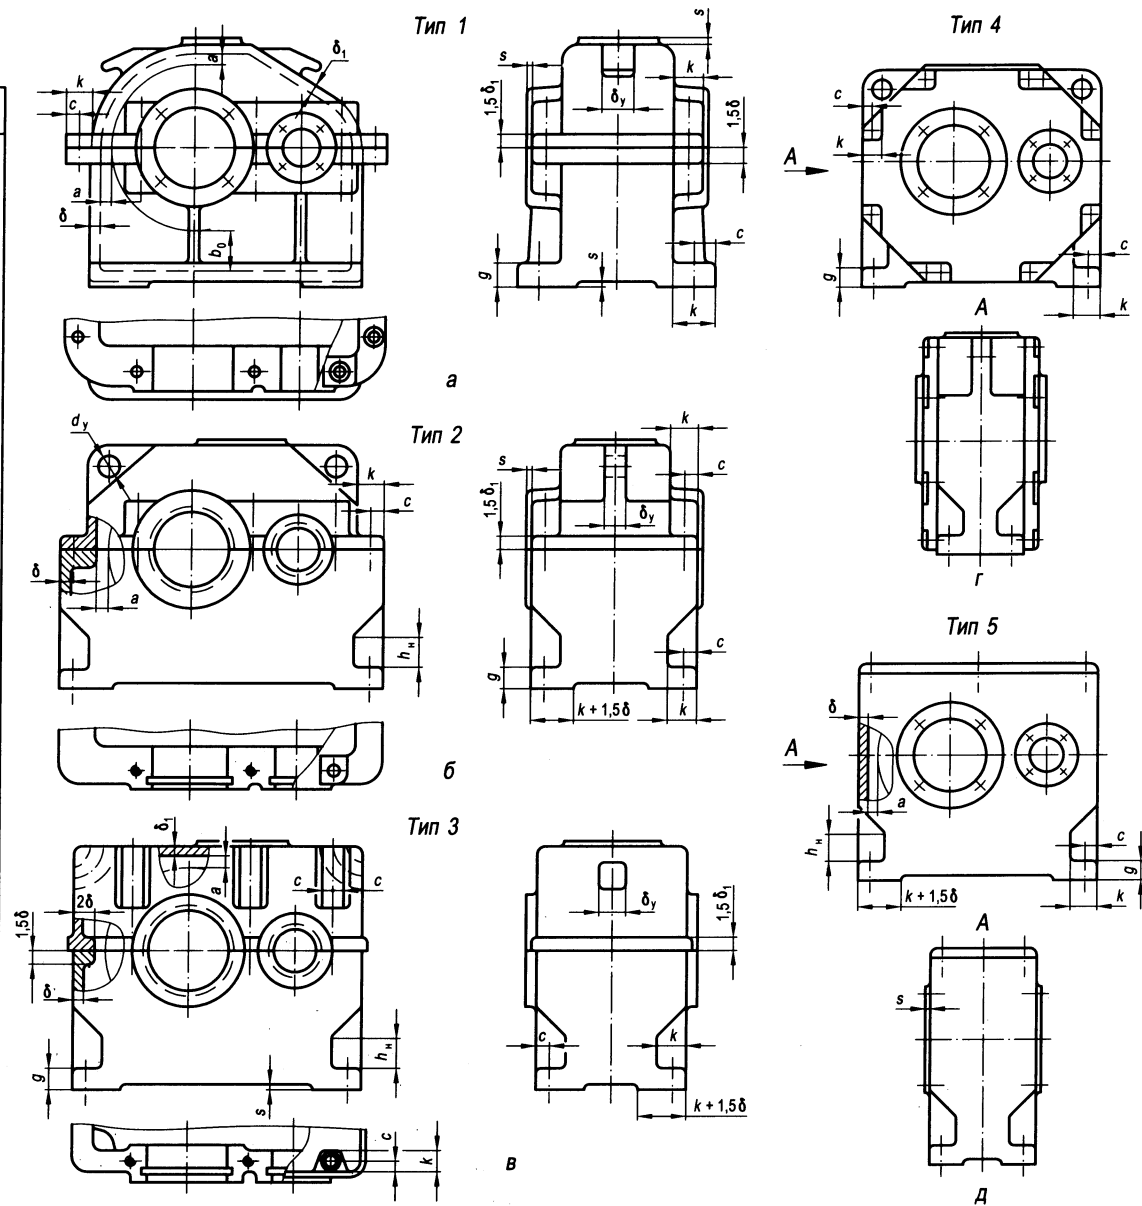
Основные типы конструкций корпусов редукторов
